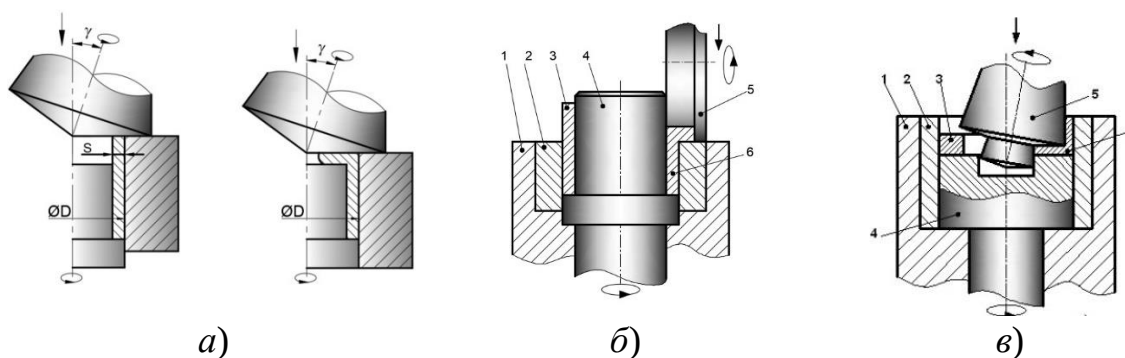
Примеры процессов торцевой раскатки при производстве осесимметричных деталей: раскатка внутреннего фланца на трубной заготовке коническим валком (а); раскатка наружного фланца на трубной заготовке цилиндрическим валком (б); раскатка внутреннего фланца из кольцевой заготовки (в)
